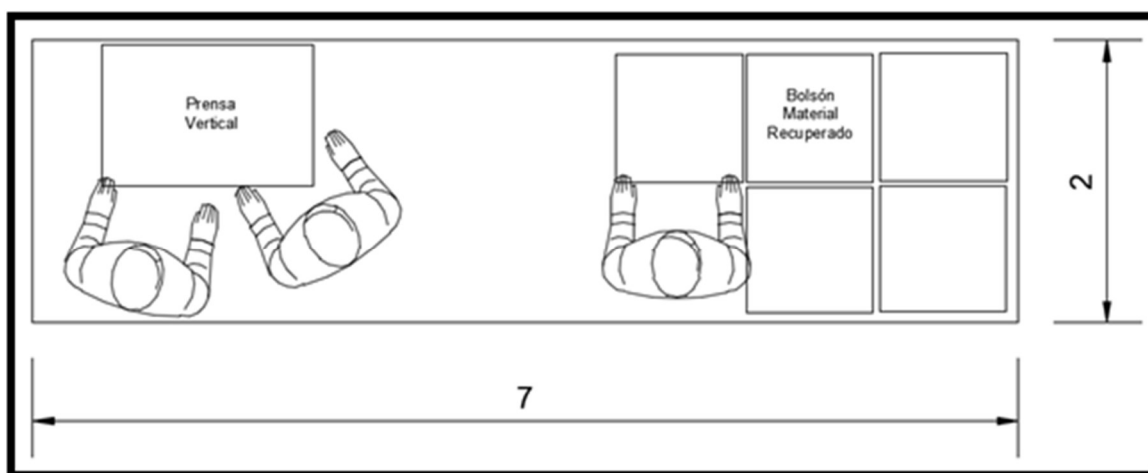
Detalle Área de Prensado – Fuente: elaboración propia
